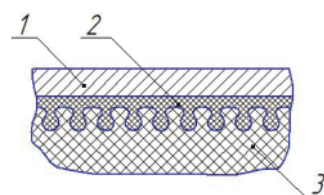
Схема скрепления заряда твердого топлива с корпусом газогенератора: 1 – корпус; 2 – профильное теплозащитное покрытие; 3 – твердое топливо
